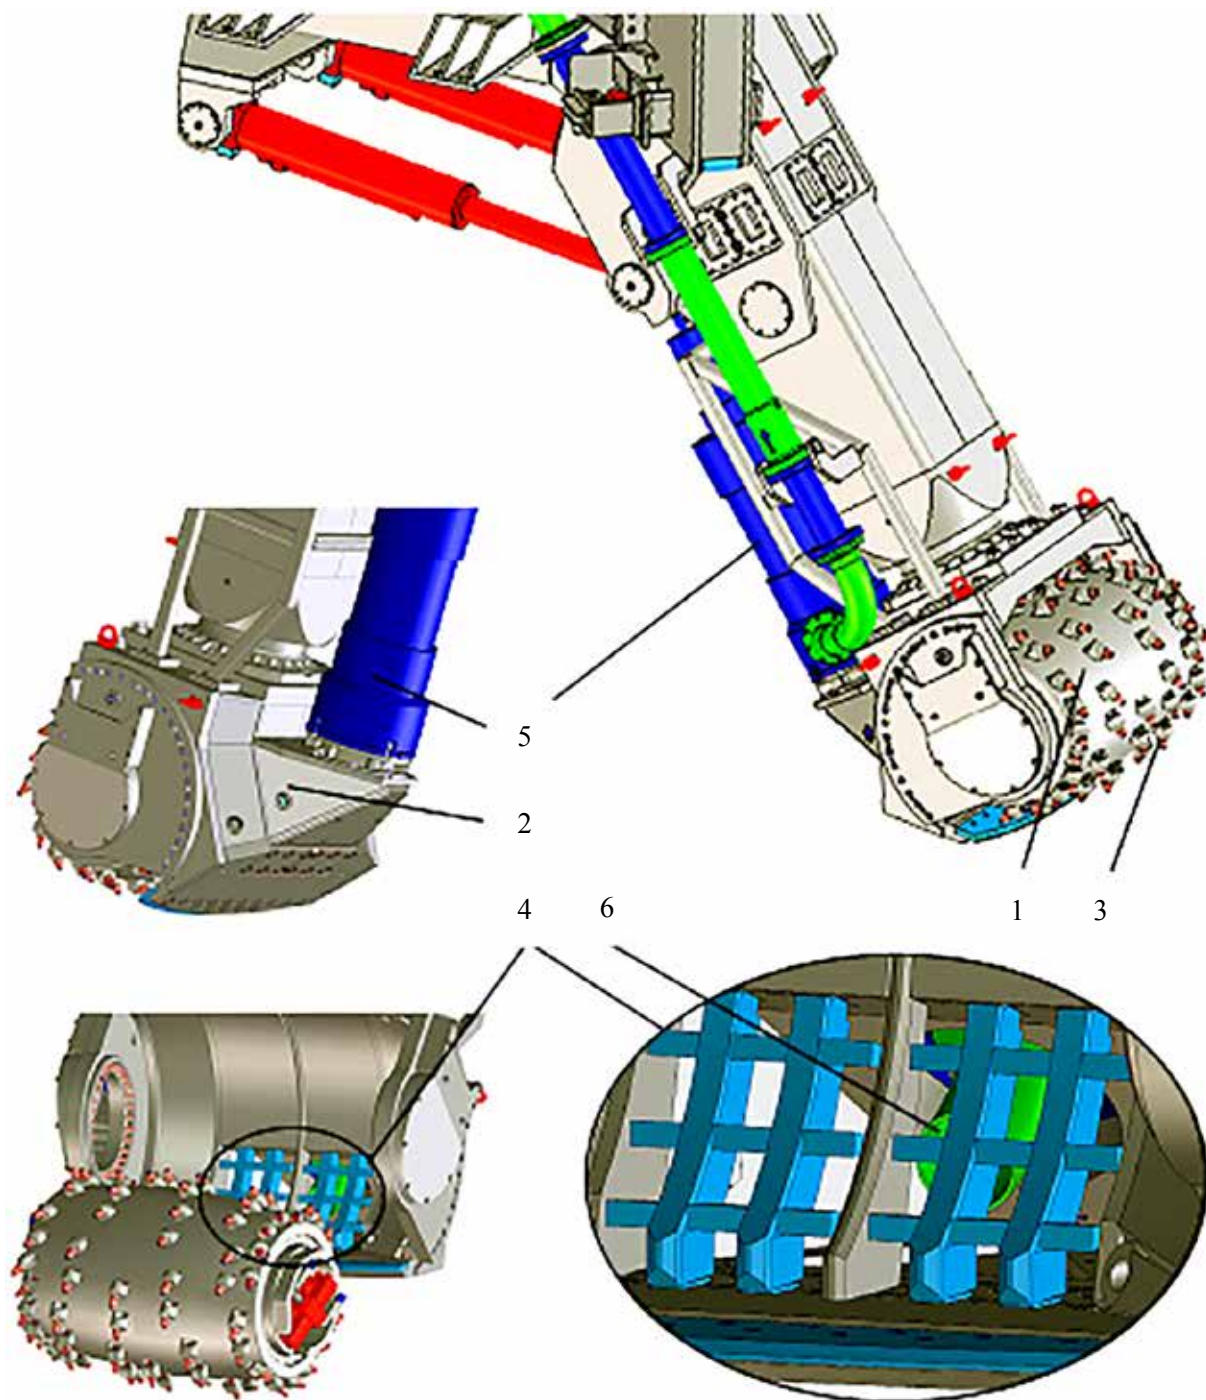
Узлы телескопической стрелы: 1 – фрез-барабан; 2 – всасывающая камера; 3 – резцы; 4 – решетка; 5 – насос для откачки пульпы; 6 – всасывающий раструб
